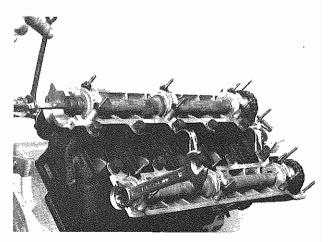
Ruotare gli assi a camme Rotating camshafts
